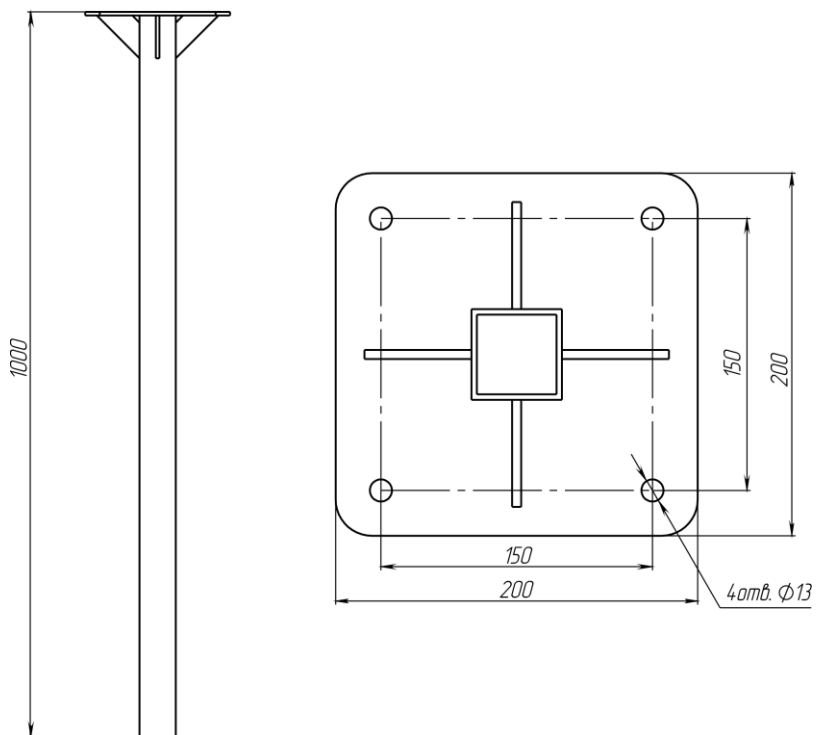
Габаритные и присоединительные размеры закладной стойки СП-01з
